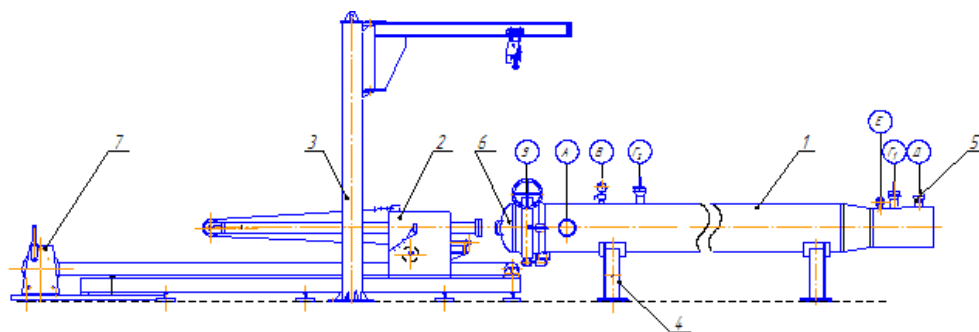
Устройство камеры запуска. 1 – корпус камеры запуска;
